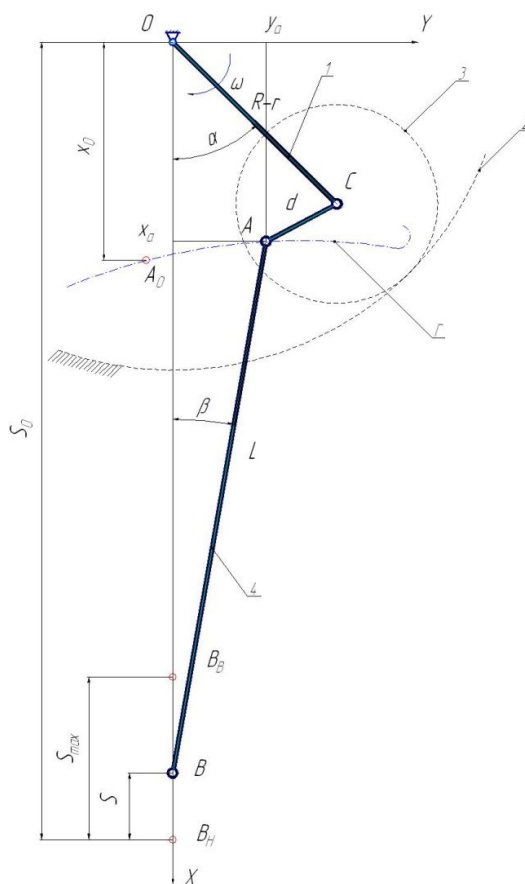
Розрахункова схема ГВМу кривошипного преса
